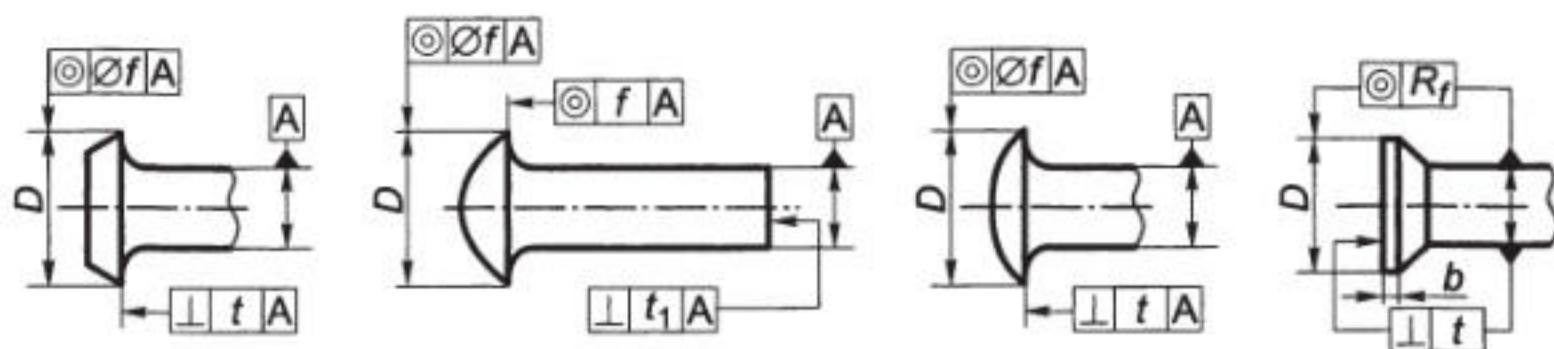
Допуски расположения поверхностей заклепок
